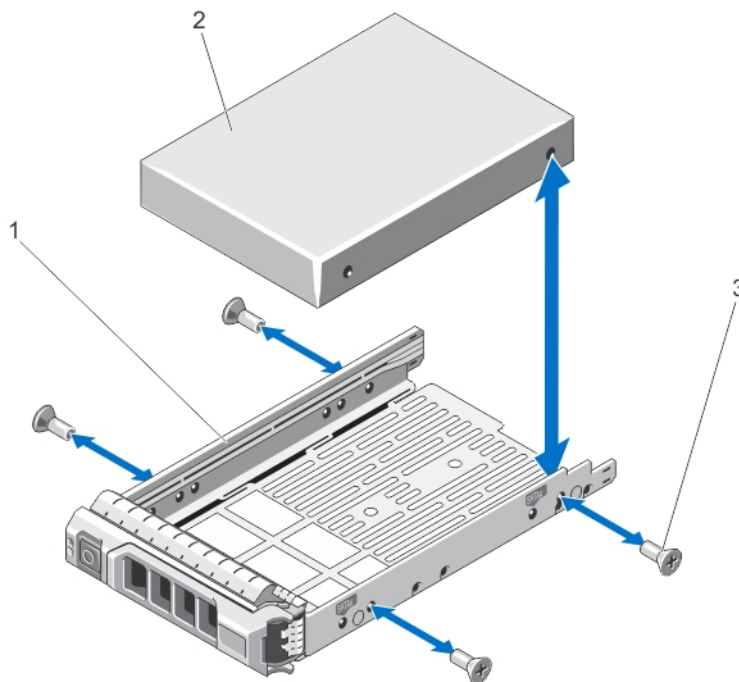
Entfernen und Installieren einer 3,5-Zoll-Festplatte aus/in einen Festplattenträger
